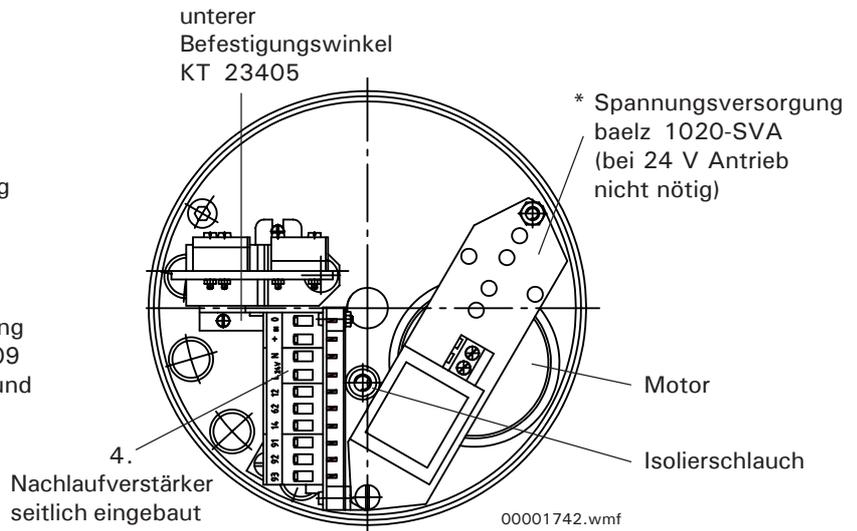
Antrieb baelz 373-E02 mit eingebautem baelz 1020
